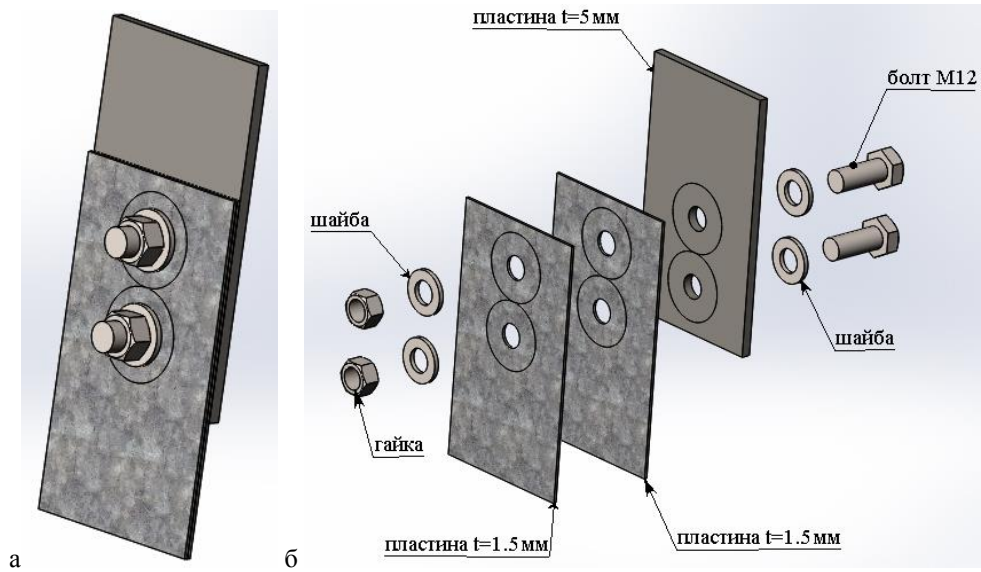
Расчетная модель: а – общий вид; б – вид с разнесенными деталями
